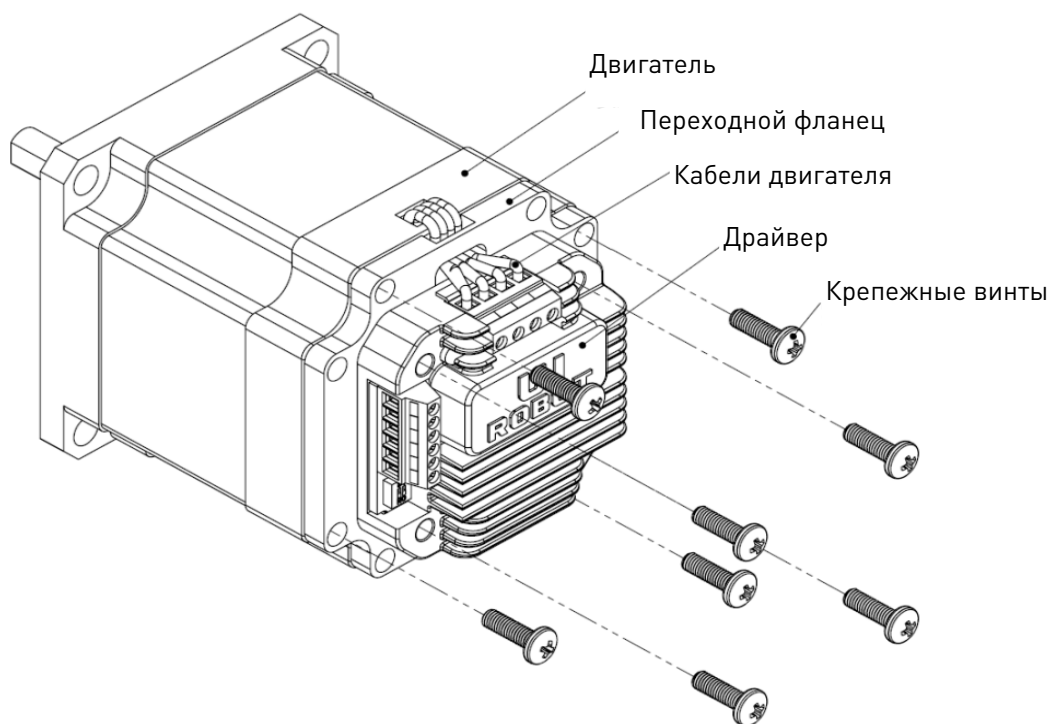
Схема установки драйвера на шаговые двигатели NEMA 23 (57мм) и больше
